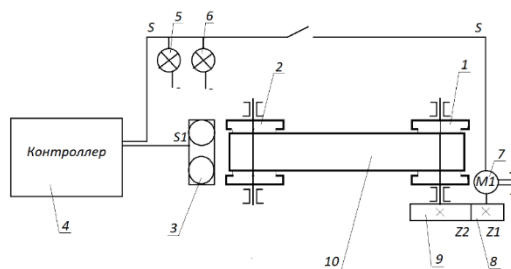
Схема кинематическая и принципиальная электрическая: 1 – барабан приводной; 2 – барабан не приводной; 3 – датчик ультразвуковой; 4 – управляющий контроллер; 5, 6 – лампы сигнальные; 7 – серводвигатель; 8 – шестерня зубчатая; 9 – колесо зубчатое; 10 – лента
